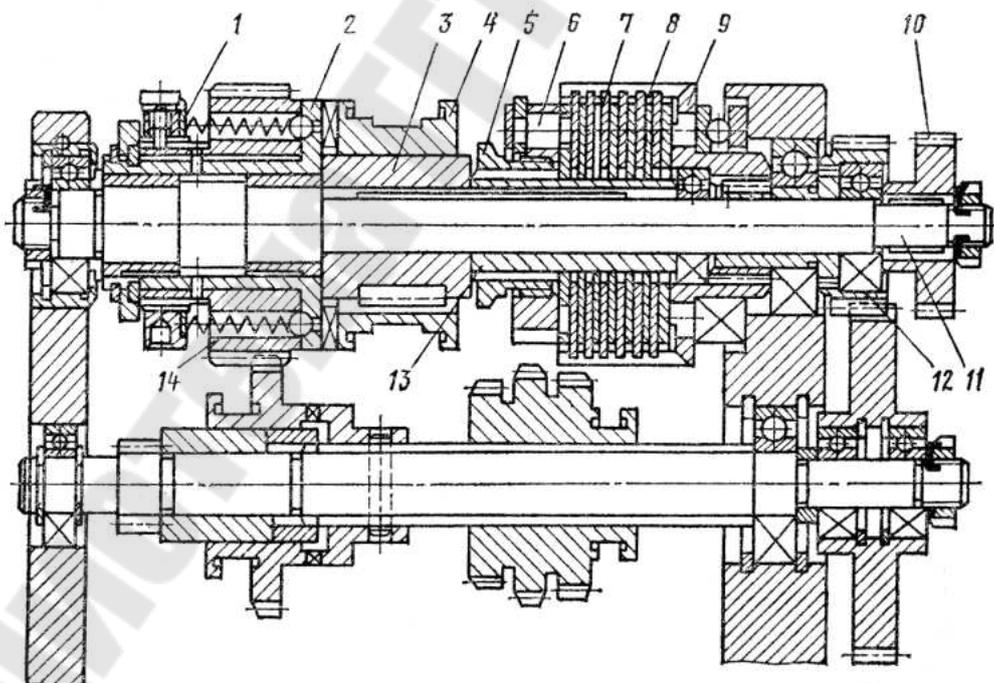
Выходной вал коробки подач станка 6Р82:
